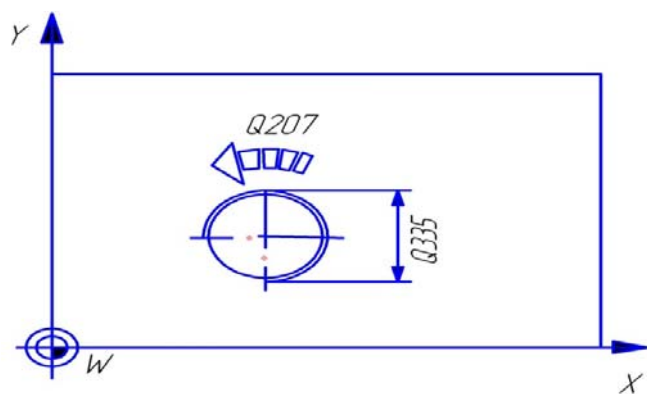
Эскиз заготовки с резьбовым отверстием, выполняемым циклом 263
